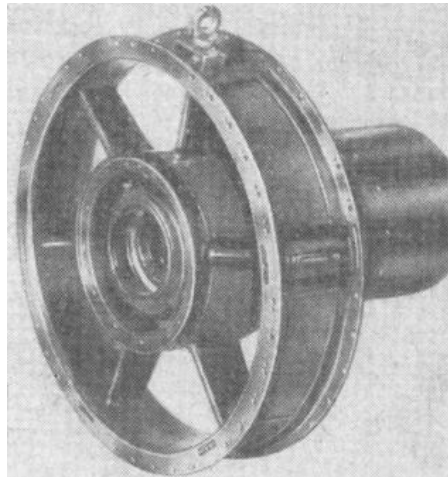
Опоры ротора свободной турбины (внешний вид)
